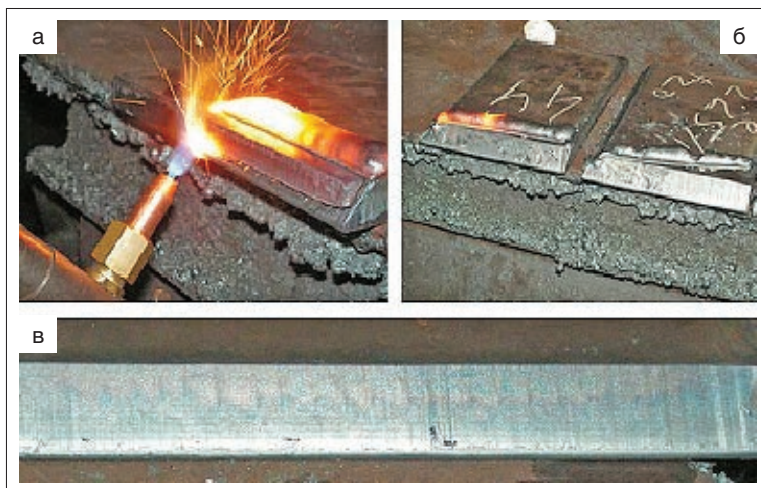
Односторонняя подготовка кромок под сварку листа толщиной 30 мм с помощью резака РГКМ-1-SR на переносной машине «Радуга» (а), поверхность реза (б, в).
